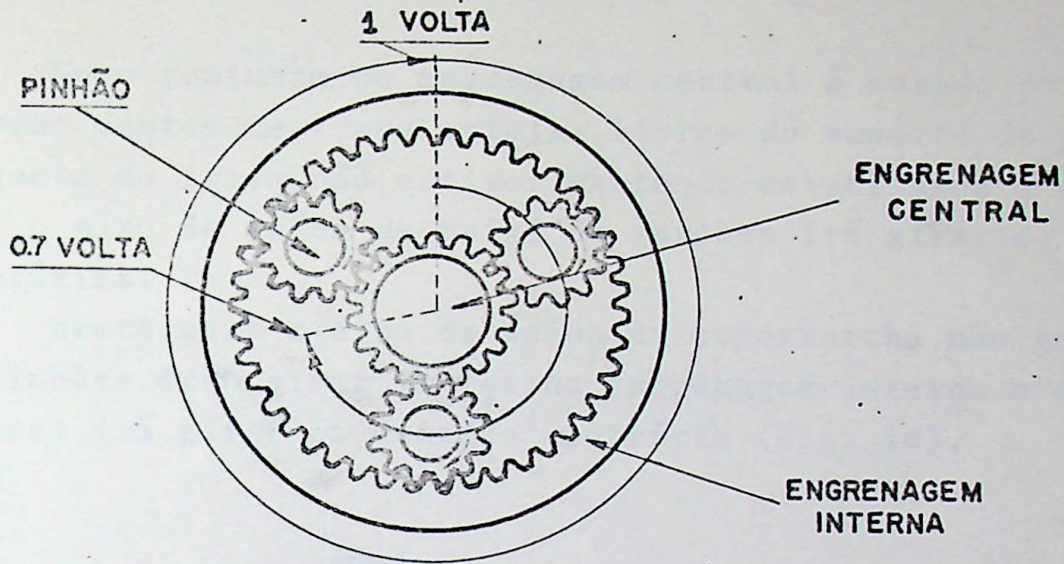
Exemplo de relação de rotação entre suporte de pinhões e engrenagem interna:
